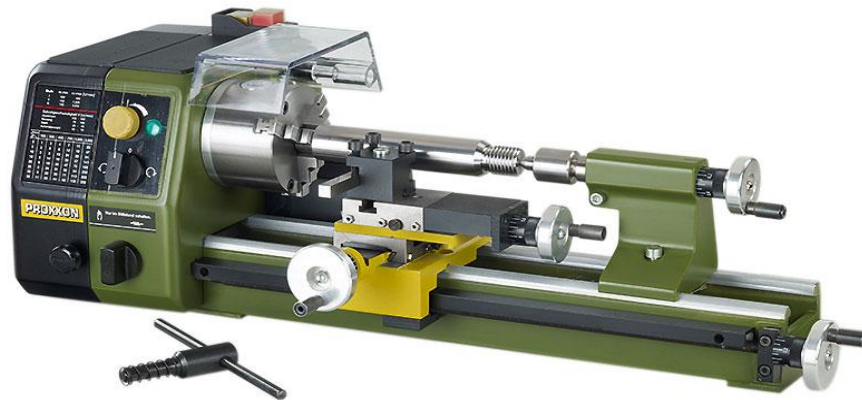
Токарный станок изготовления детали вала-шестерня
